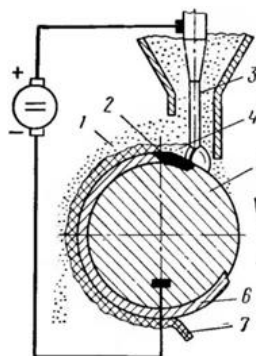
Схема наплавки под слоем флюса: 1 – нерасплавленный флюс; 2 – жидкий металл; 3 – электрод; 4 – расплавленный шлак; 5 – деталь; 6 – наплавленный металл; 7 – шлаковая корка
